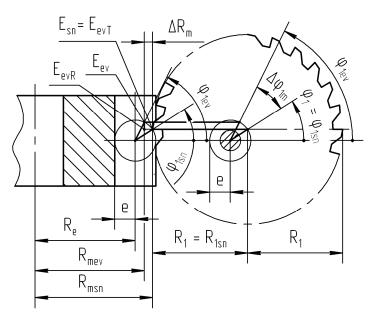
Схема нарізання зубців циліндричного колеса способом РКЗД
